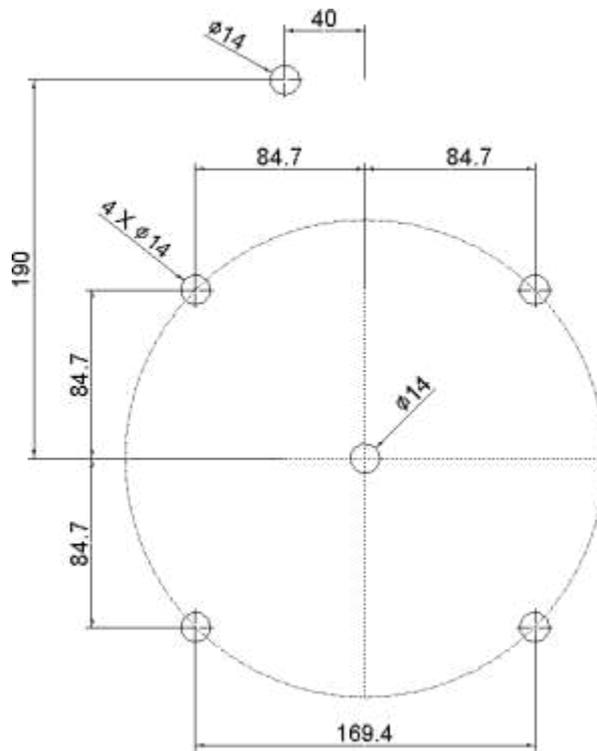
LAYOUT DE FURAÇÃO DO TETO
